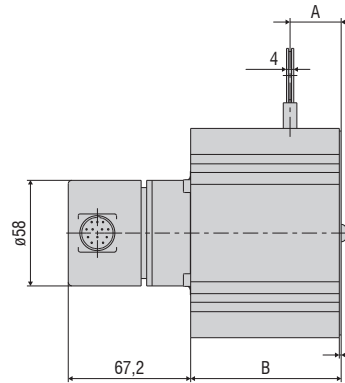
Maßzeichnung WDS- ... - P115 - SR - SSI
